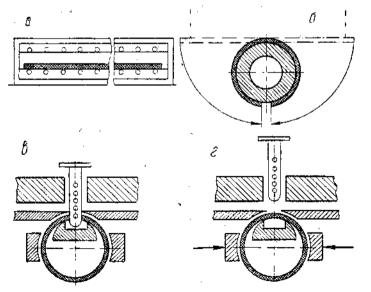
Технологический процесс изготовления полиэтиленовых труб: а—разогрев заготовки детали из полиэтилена в термошкафу. б—формование разогретой заготовки в трубу, в—прогрев свариваемого шванагретой линейкой, г—стыковая сварка продольного шва.
